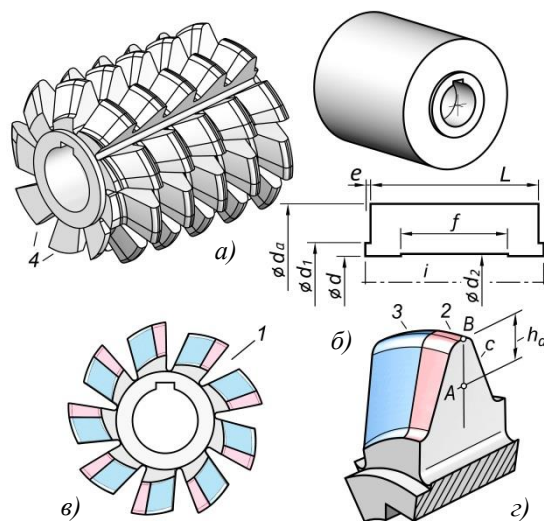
Конструкция фрезы: а – общий вид; б – заготовка; в – канавки; г – зуб
